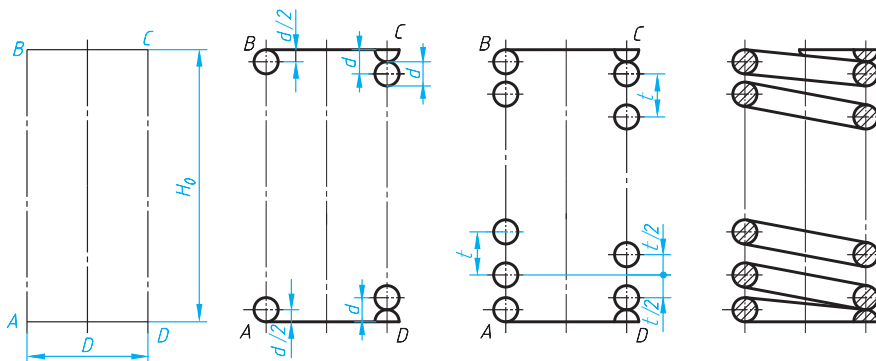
圆柱螺旋压缩弹簧的画图步骤
